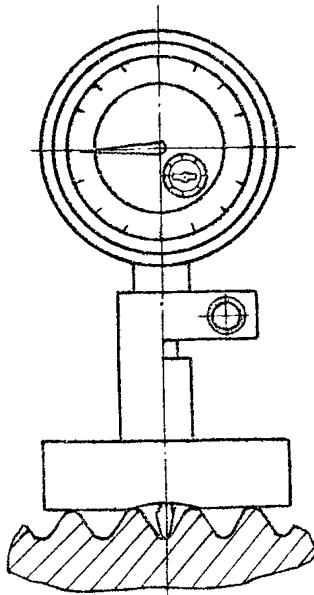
Контроль высоты профиля резьбы индикаторным прибором.
